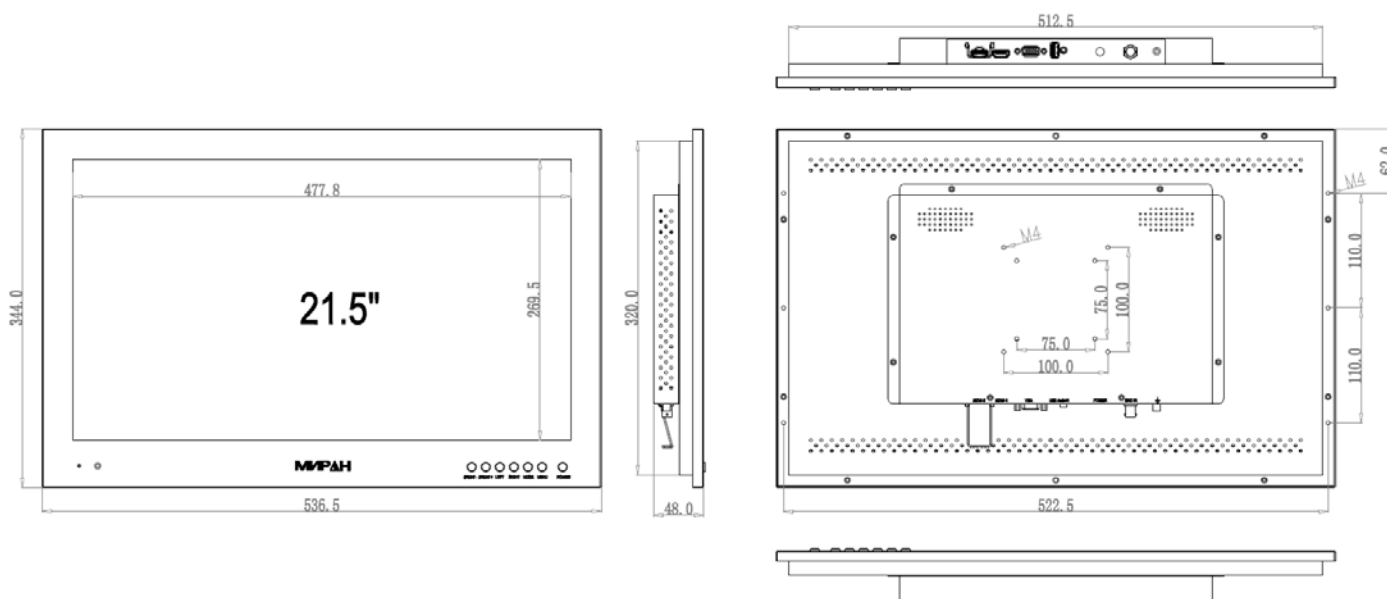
Габаритный чертеж монитора ИВМ-22ЖК.
